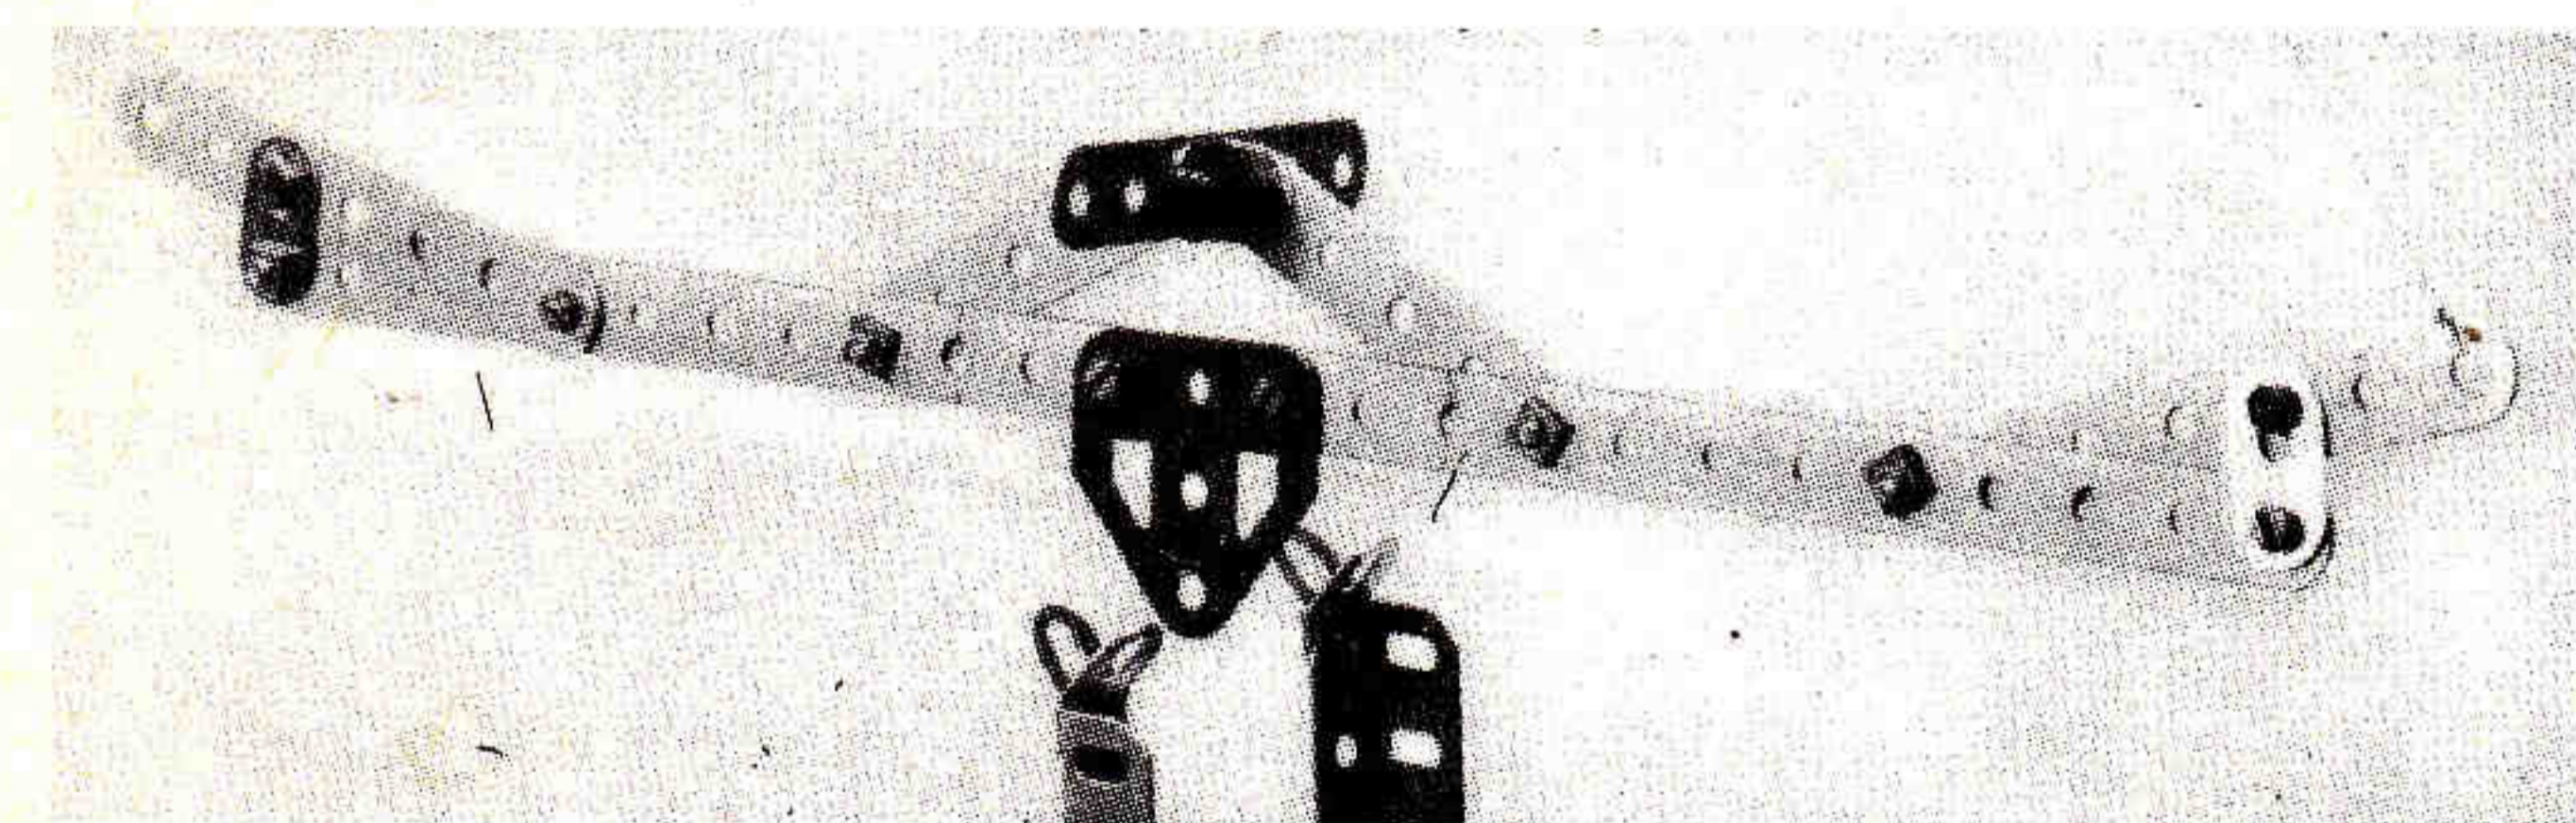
Vue du fléau, montrant sa structure et sa disposition sur les couteaux du support.
